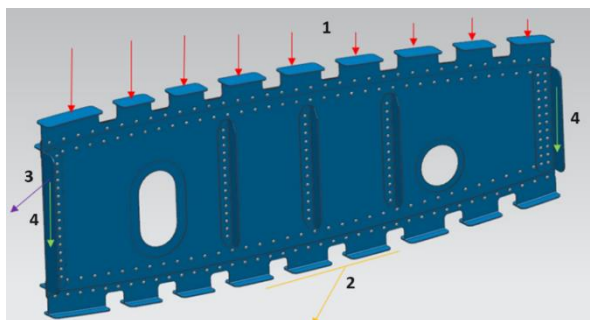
Нагрузки, действующие на силовую нервюру: красная (1) – распределенная воздушная нагрузка, желтая (2) и фиолетовая (3) – нагрузки от двигательной установки, зеленая (4) – нагрузка от лонжерона
